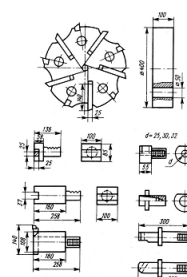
Типовые резцовые блоки крепления цилиндрическим хвостовиком с реечным зацеплением
